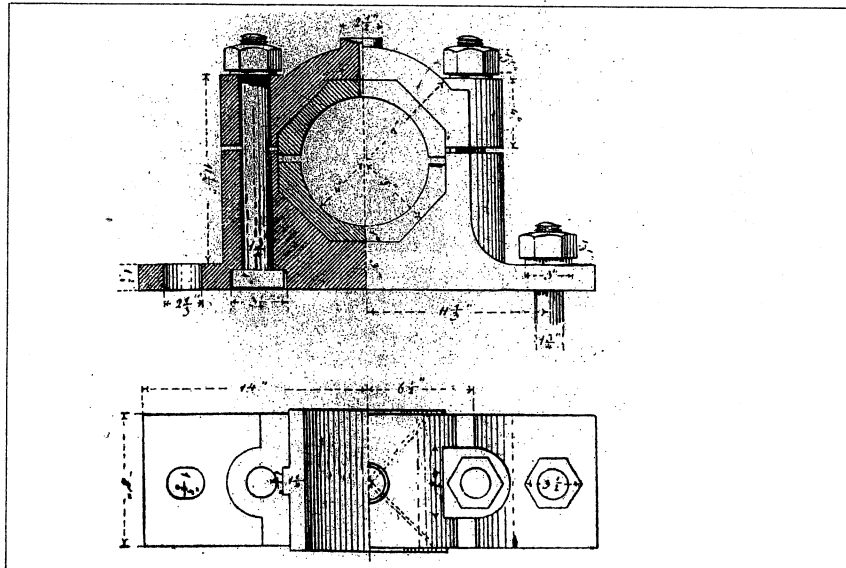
/1: Baugruppenzeichnung eines Stehlagers (um 1830)
